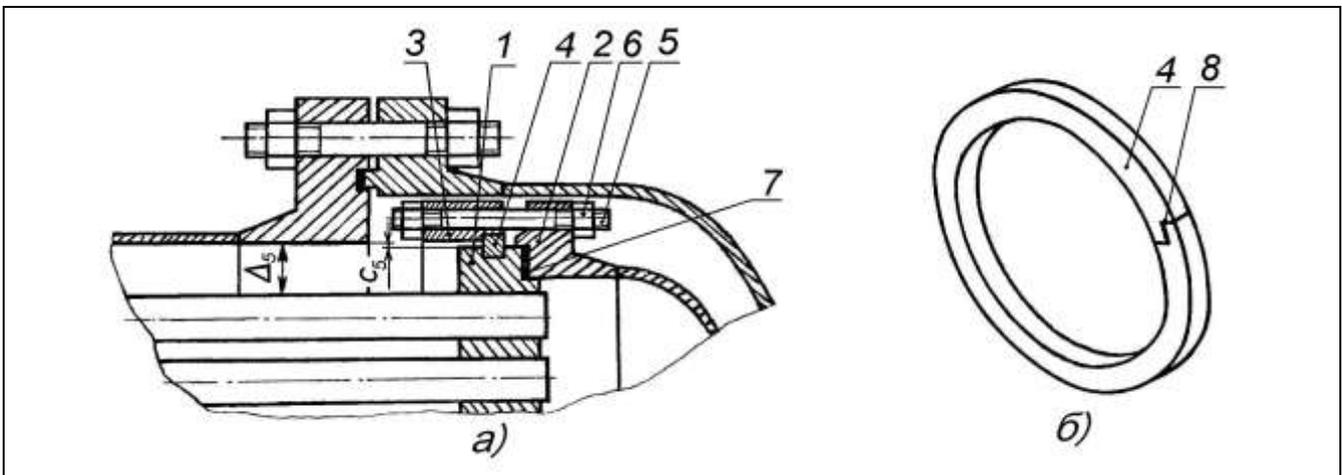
Плавающая головка с разрезным закладным кольцом 4 и стяжным накидным фланцем 3: а) – общий вид плавающей головки; б) – внешний вид закладного кольца 4 с одним замковым разъемом 8 перед началом сборки узла
